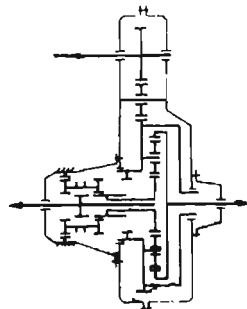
Схема раздаточной коробки с планетарным редуктором автомобиля Magirus L15, D22
